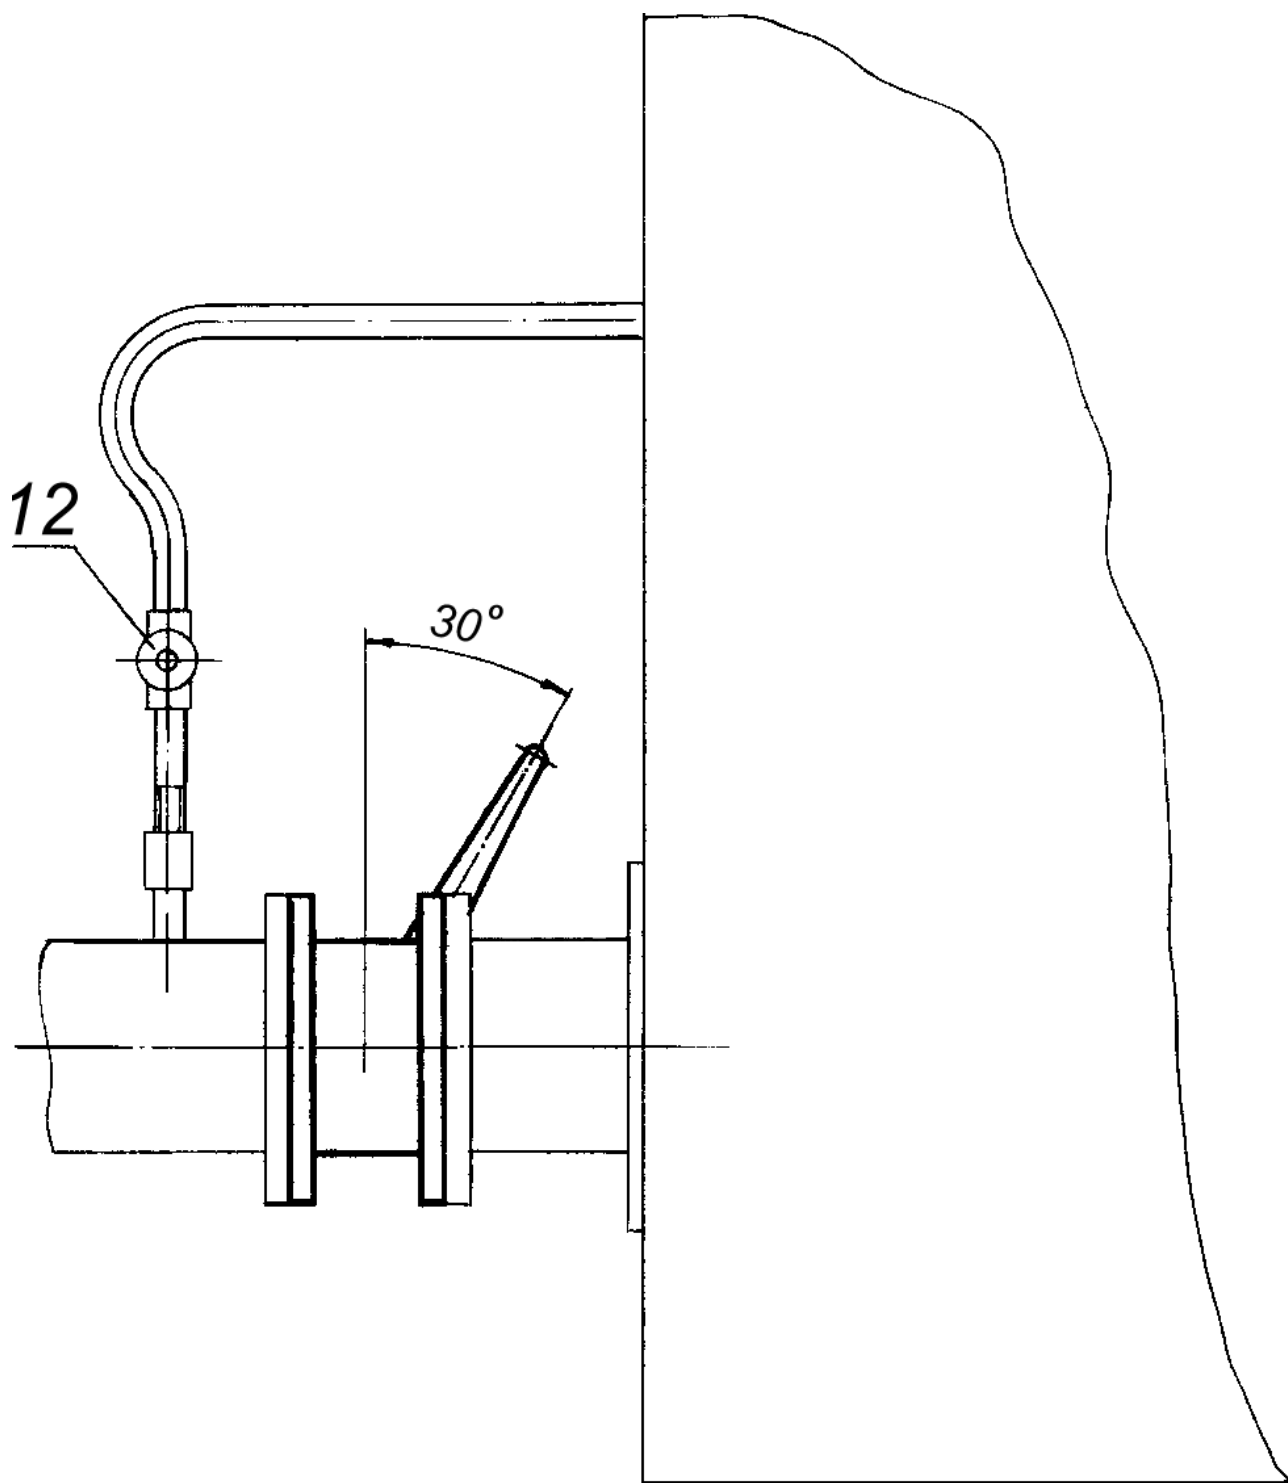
Установка механизма управления МУ-250р на резервуаре
